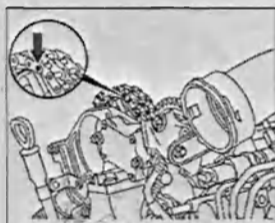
При установке цепи на опорный шпindel убедитесь, что упорный палец расположен напротив левого пальца звена цепи.
